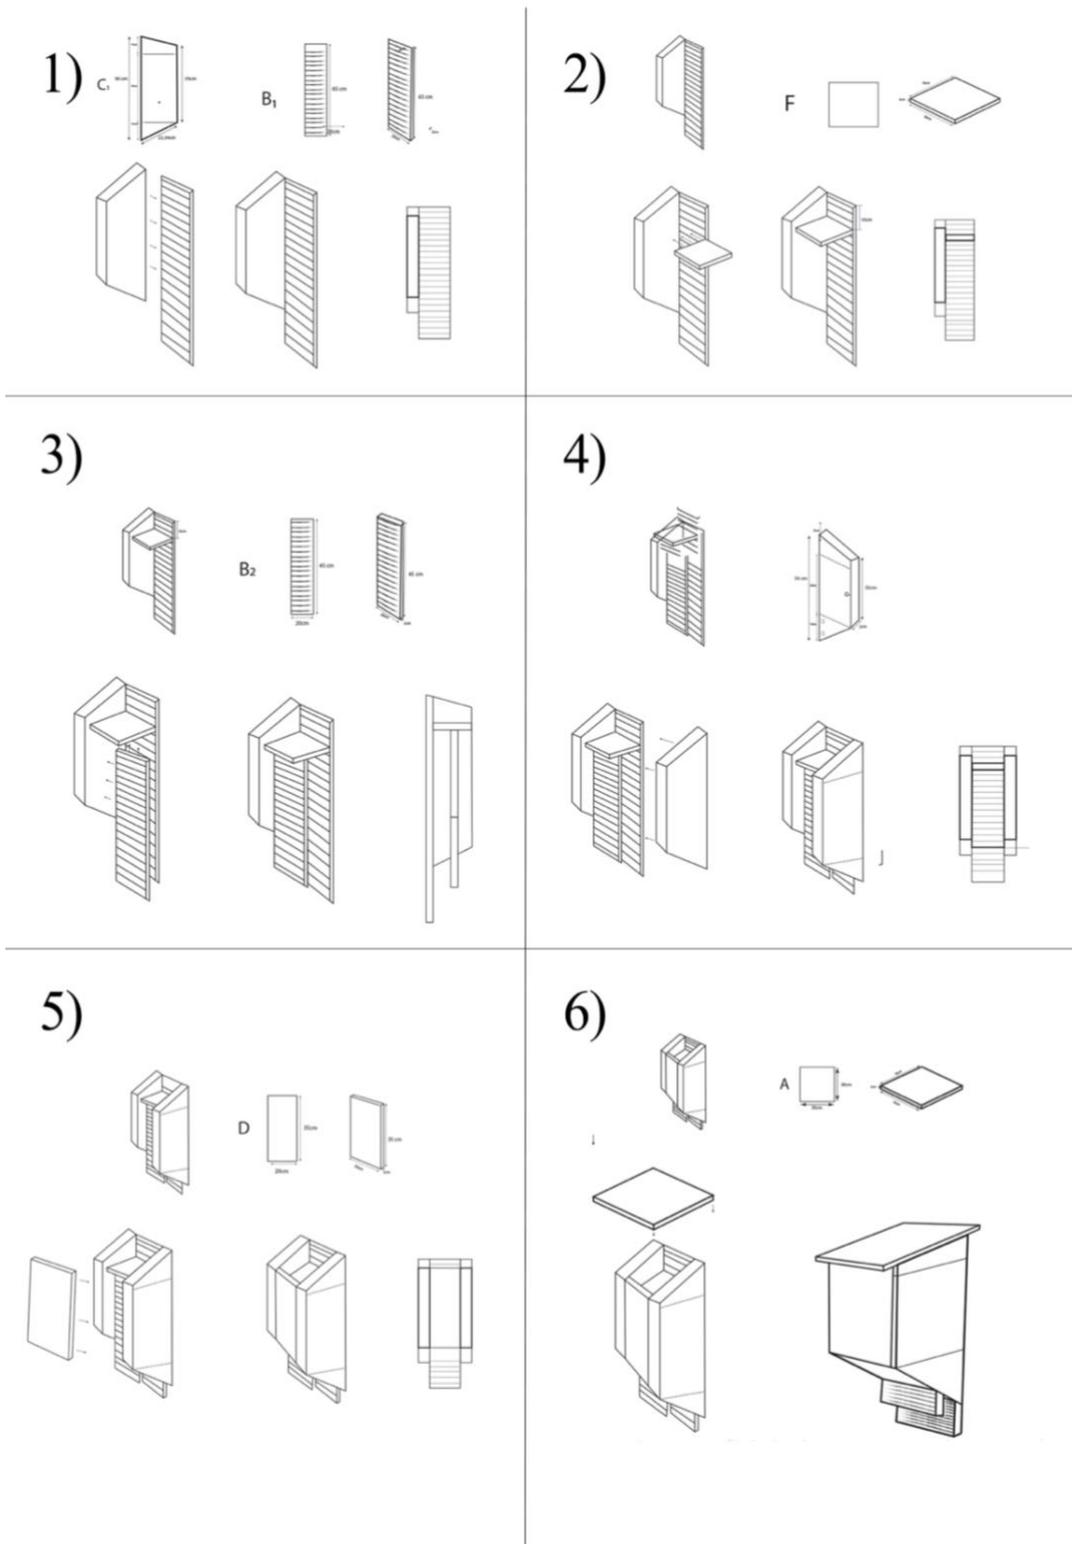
Procedimiento general de la construcción de los RA. 1) Unión de las piezas “C1” con “B1”. 2) colocación de la pieza “F” 10 cm por debajo de la parte superior. 3) Colocación de la pieza B2. 4) Colocación de la pieza “C2” a la estructura ya formada. 5) Colocación de la pieza “D”. 6) Colocación de la pieza “A”.
